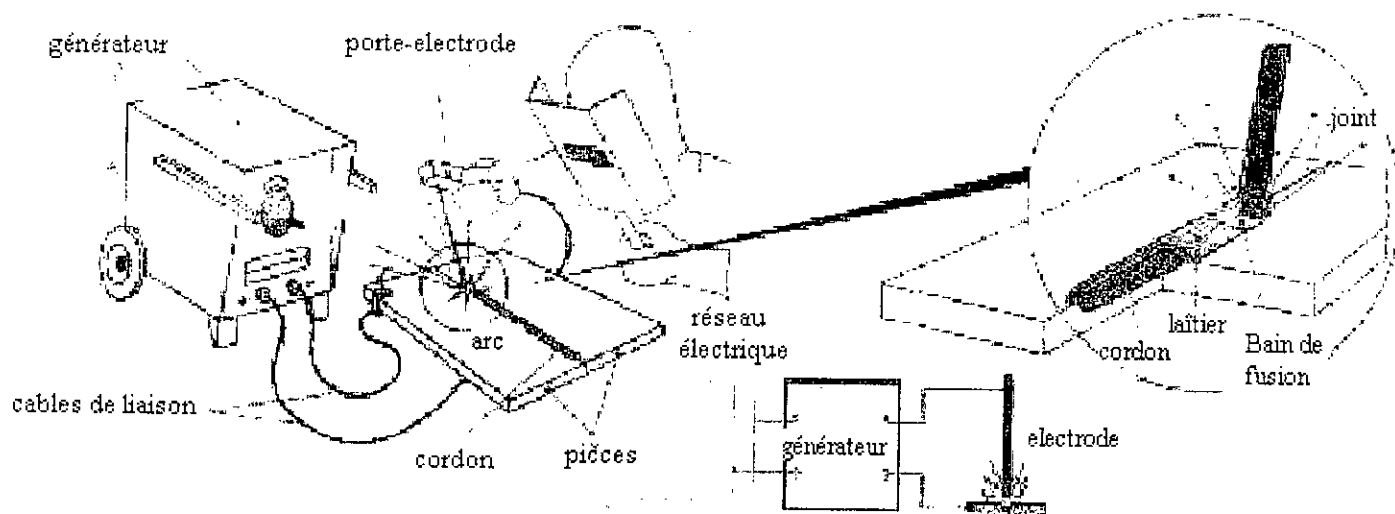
soudage à l'électrode enrobée : principe
